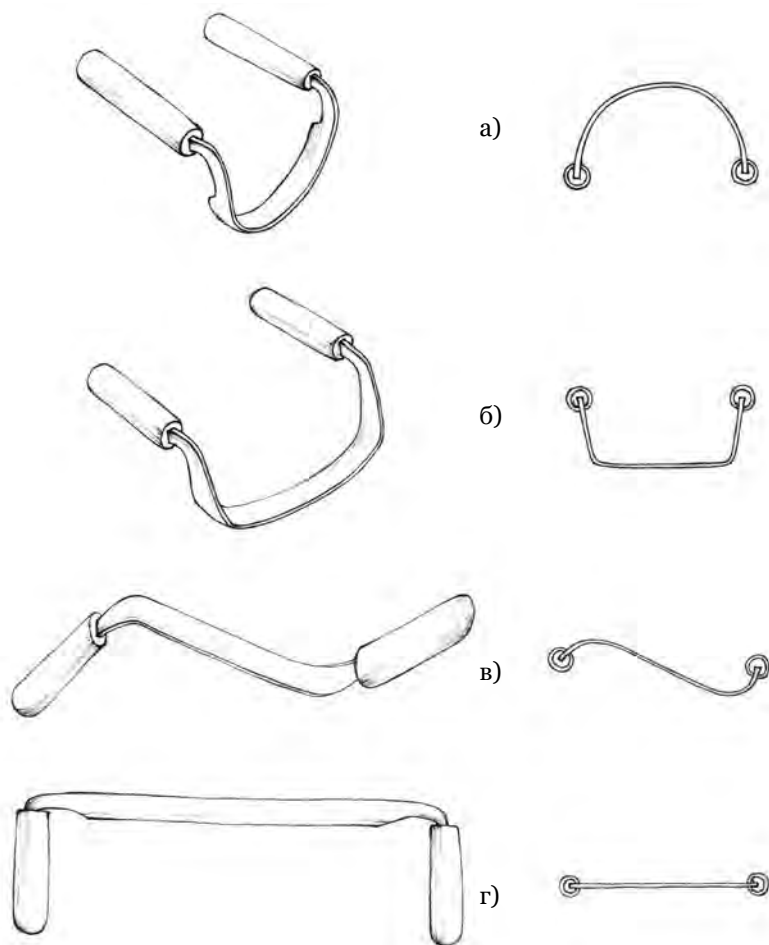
Скобели: а) круглый; б) прямой; в) угловой; г) струг
